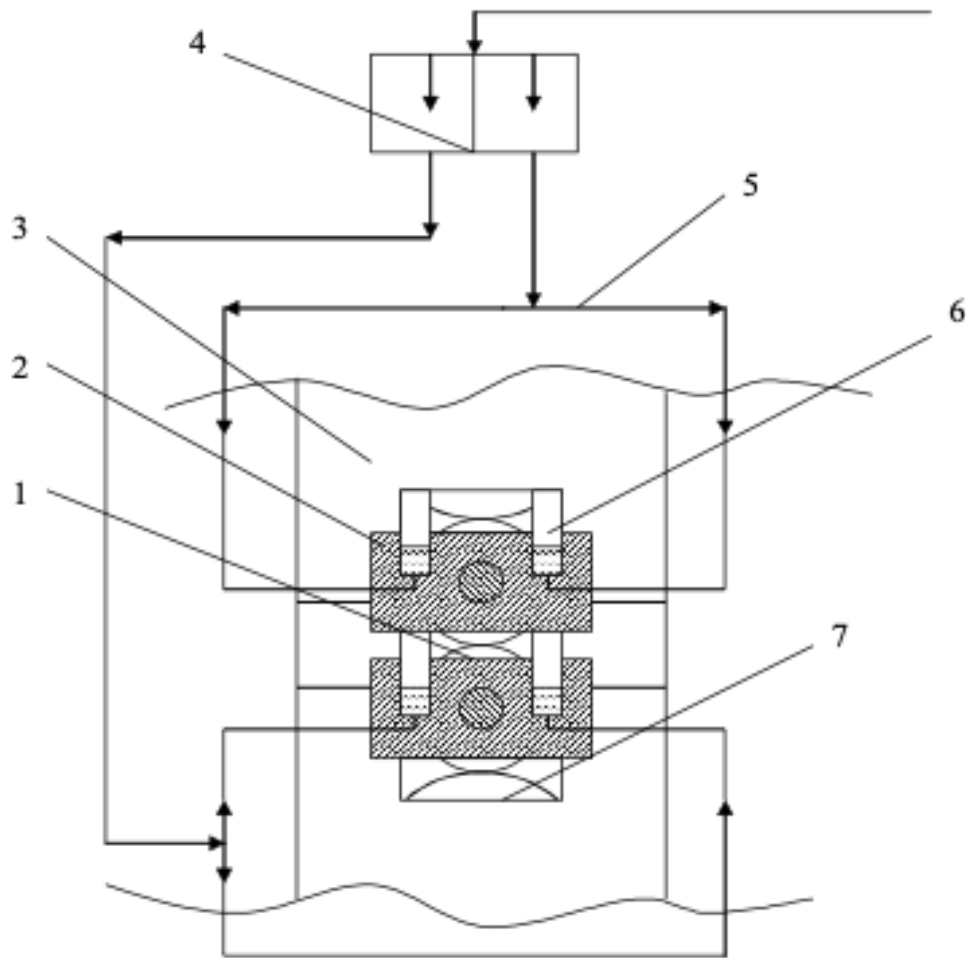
Система гідровигину: 1 - робочі валки; 2- подушка робочих валків; 3- подушка опорних валків; 4-перикидний клапан; 5-магістралі подачі масла; 6- гідравлічні плунжери; 7- опорний вал.
